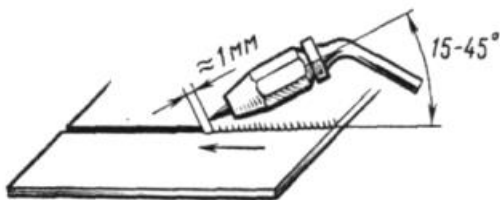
Положение сопла горелки относительно сварного шва
